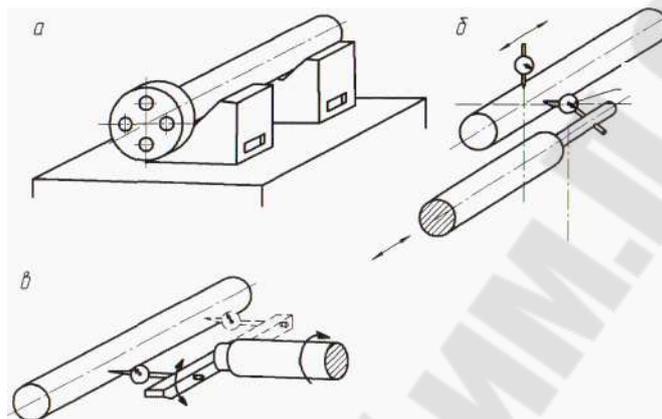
Установка (а) и выверка (б, в) заготовок на призмах
